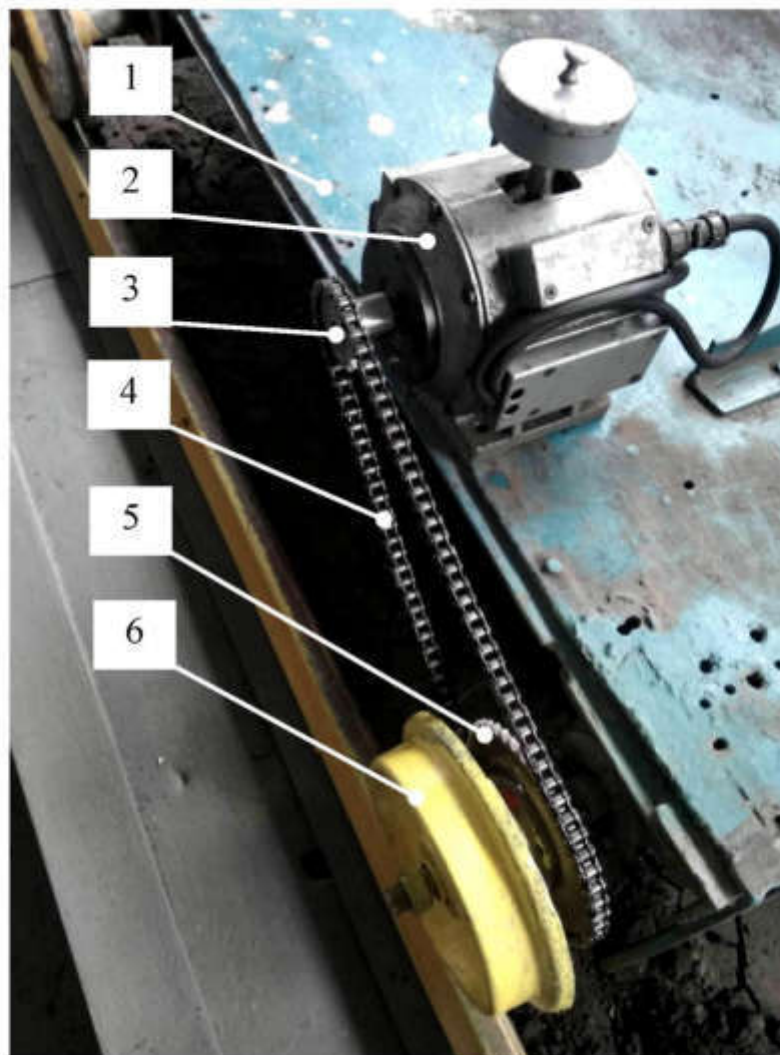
Опытный образец подвижного модуля с динамическим стабилизатором устойчивости его движения
